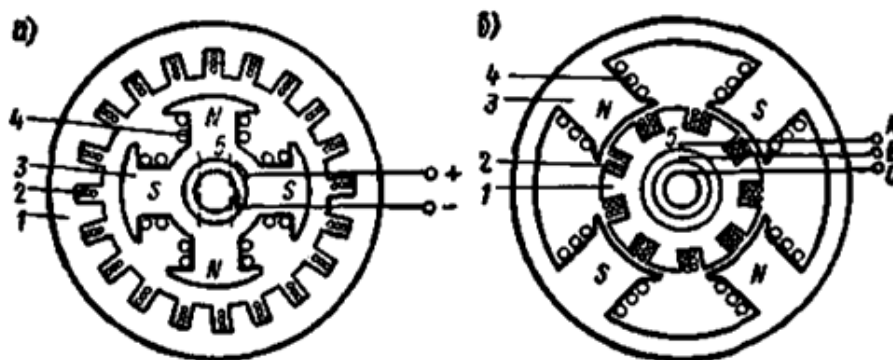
Конструктивная схема синхронной машины с неподвижным и вращающимся якорем: 1 – якорь; 2 – обмотка якоря; 3 – полюсы индуктора; 4 – обмотка возбуждения; 5 – кольца и щетки
